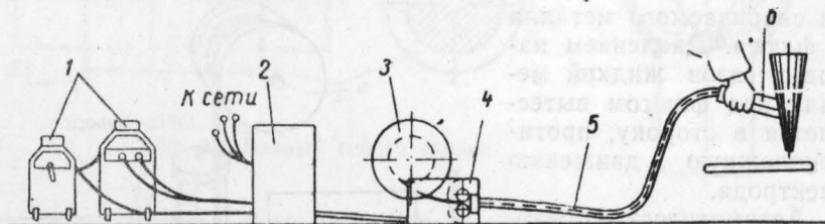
Схема полуавтоматической сварки под флюсом
